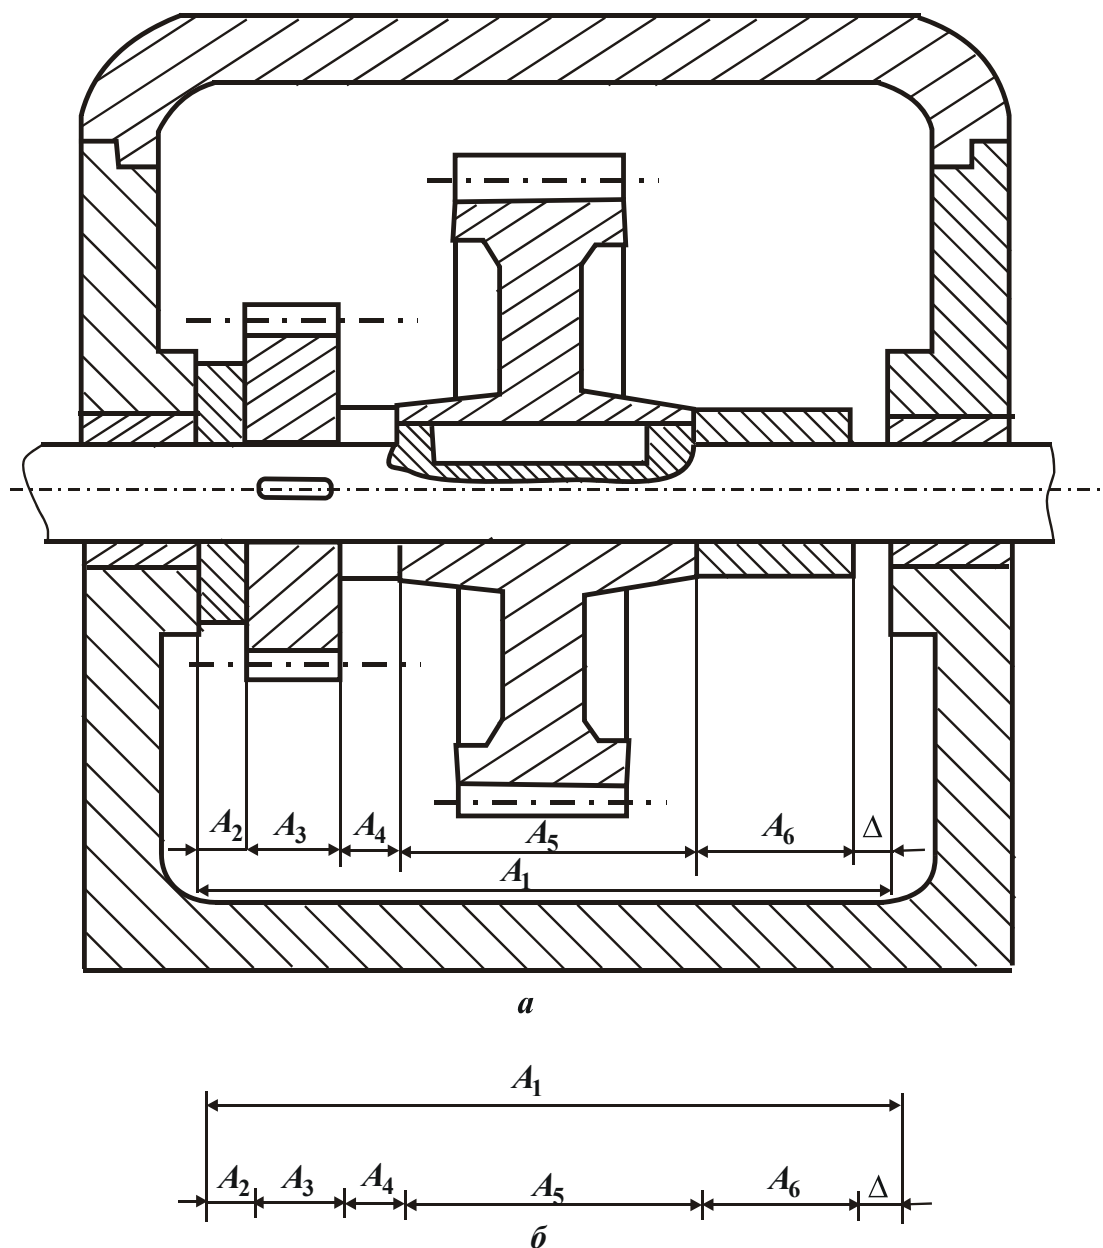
Схемы: а – осевого разреза редуктора, б – сборочной размерной цепи.
